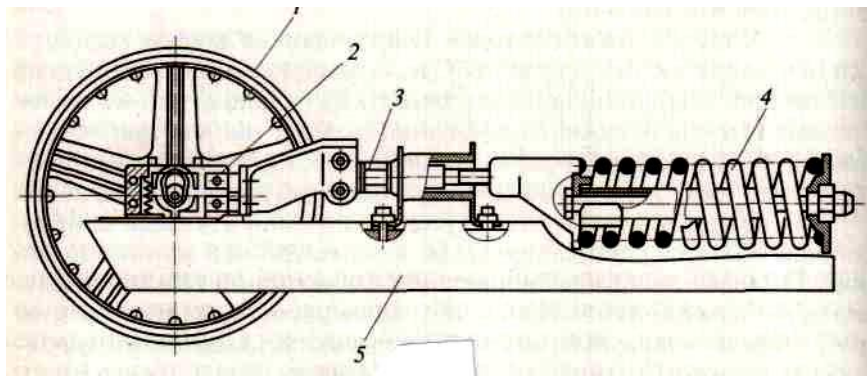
Схема установки направляющего колеса на ползуне:
